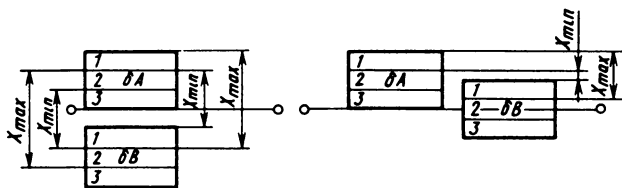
Стандартное и нестандартное расположение полей допусков при селективной сборке
